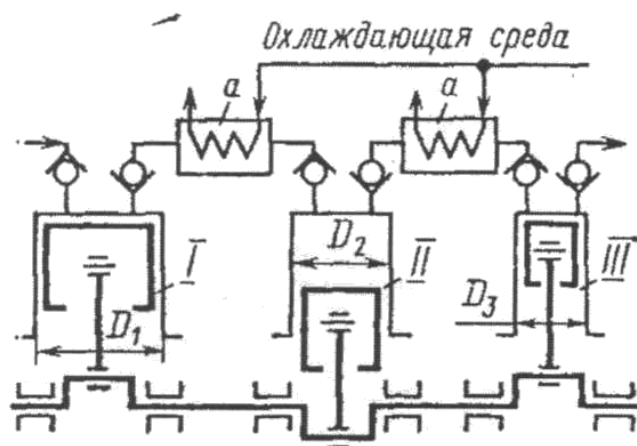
Принципиальная схема поршневого трехступенчатого компрессора с рядным расположением цилиндров
